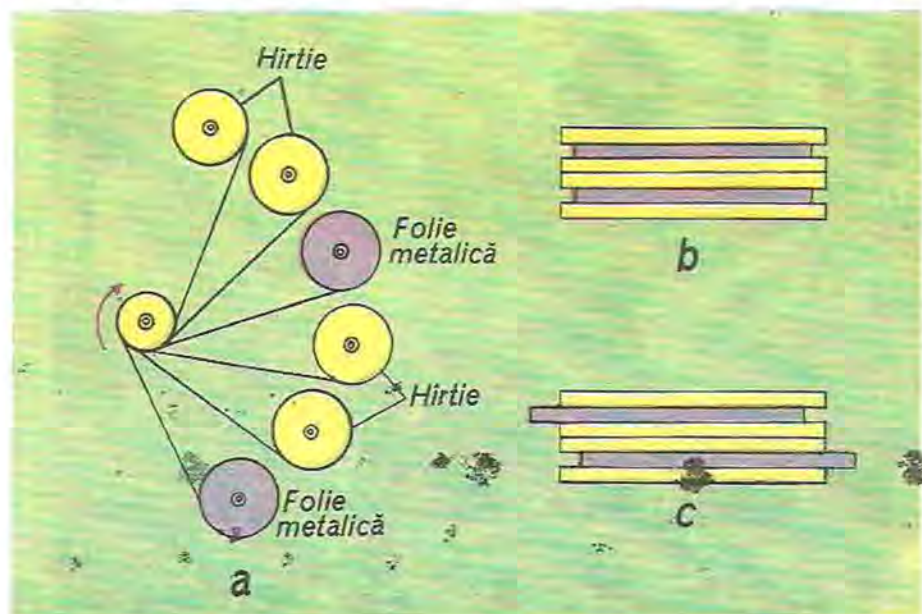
Construcția condensatoarelor cu hîrtie: a) schema de bobinare; b) secțiune prin bobina cu armături suprapuse; c) secțiune prin bobina cu armături decalate.
